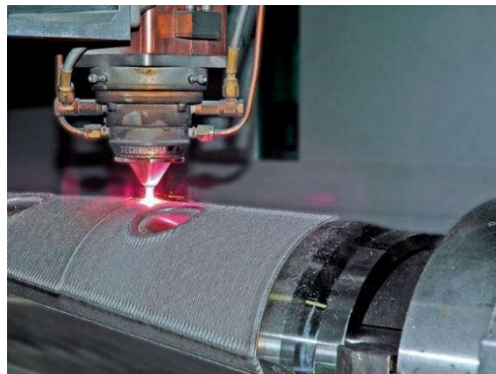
Beschichtung einer Bohrwerkzeug[Quelle: Technogenia]
